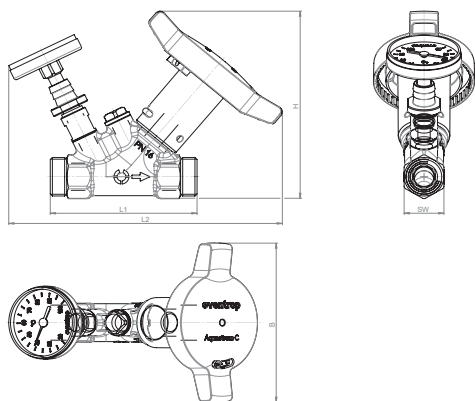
Размеры Вид сбоку / Вид спереди Внешняя резьба
